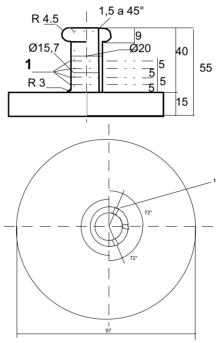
Cilindro cavo di bronzo, chiuso da un lato; vista in pianta e sezione verticale
